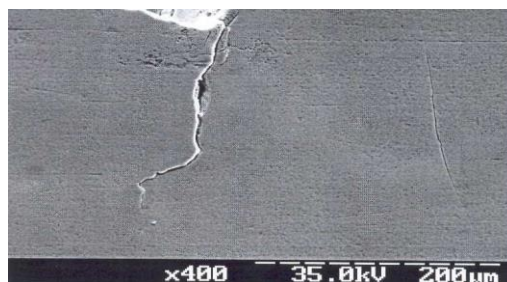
Розвиток тріщини на поверхні обійми роликового підшипника
